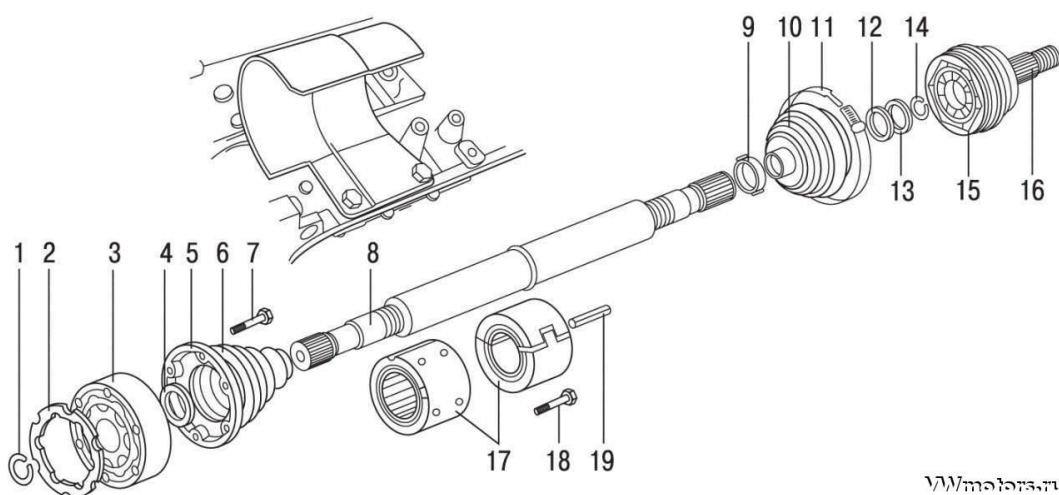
Привод переднего колеса Фольксваген Пассат Б3-Б4
